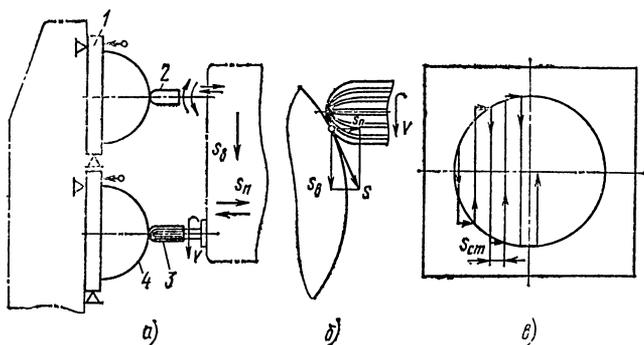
Схема обработки поверхностей на копирующе-фрезерном станке
